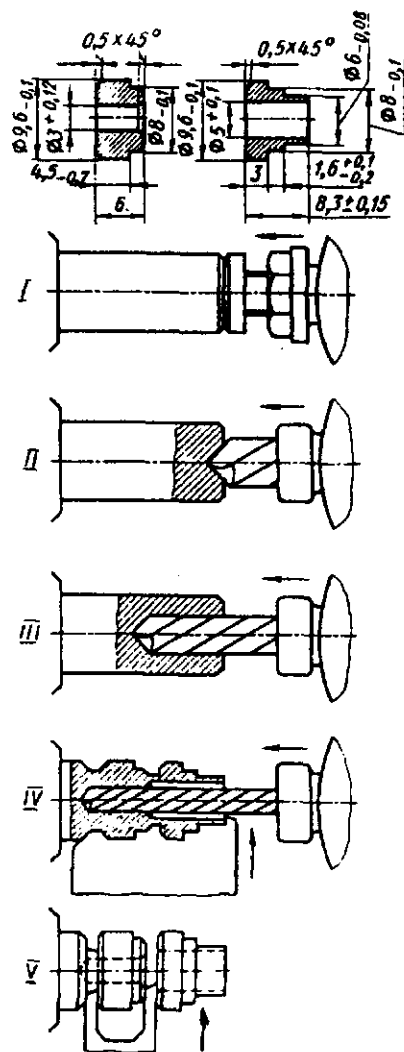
Наладка одношпиндельного токарно-револьверного автомата для одновременной обработки деталей двух наименований
